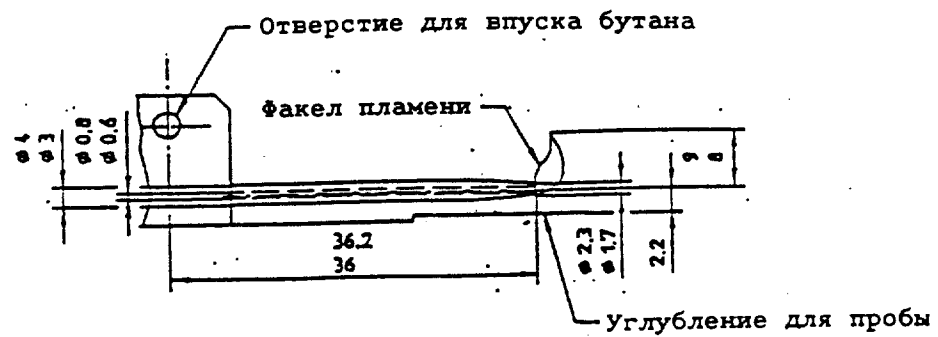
Форсунка для подачи газа и регулирования положения факела пламени
